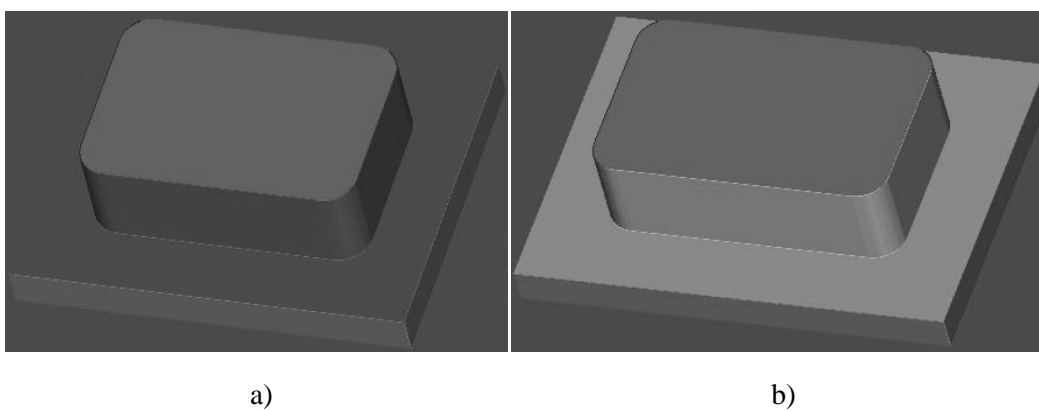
a) Punzón de tarjeta maquinado con cortador de 12.7 [mm]. b) Punzón de tarjeta maquinado con cortador de 4.76 [mm].
